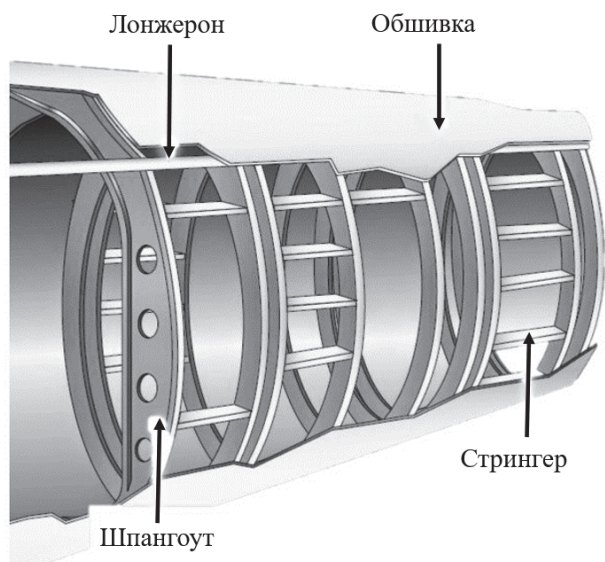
Типовая конструкция фюзеляжа ЛА и используемые детали машин
